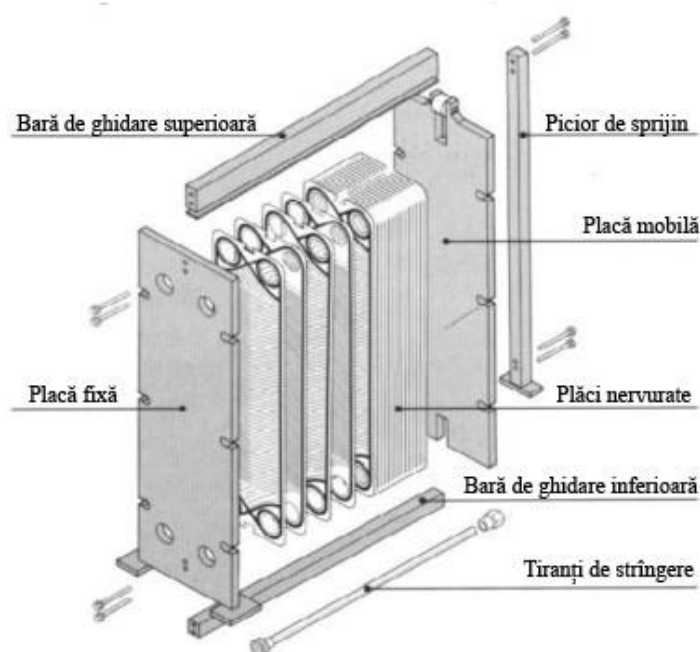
Detalii privind construcția SC din PT-UO
